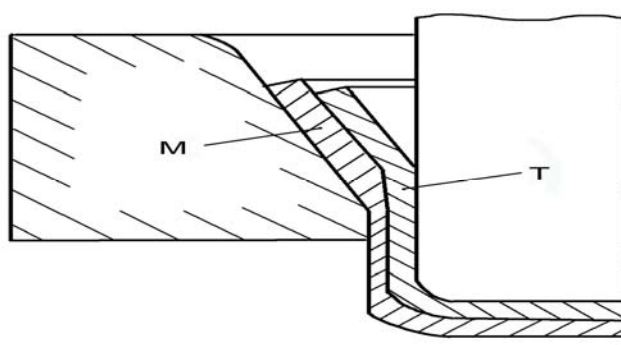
Схема комбинированной вытяжки двухслойной заготовки:
